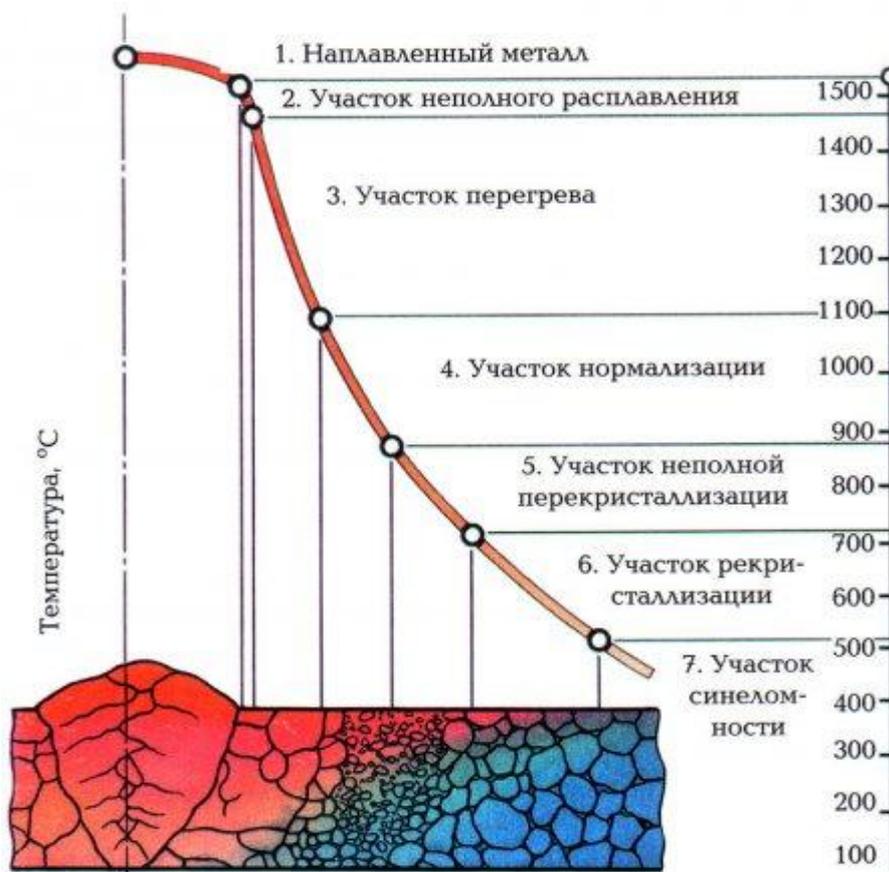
Термический цикл сварного соединения низкоуглеродистой стали при сварке
